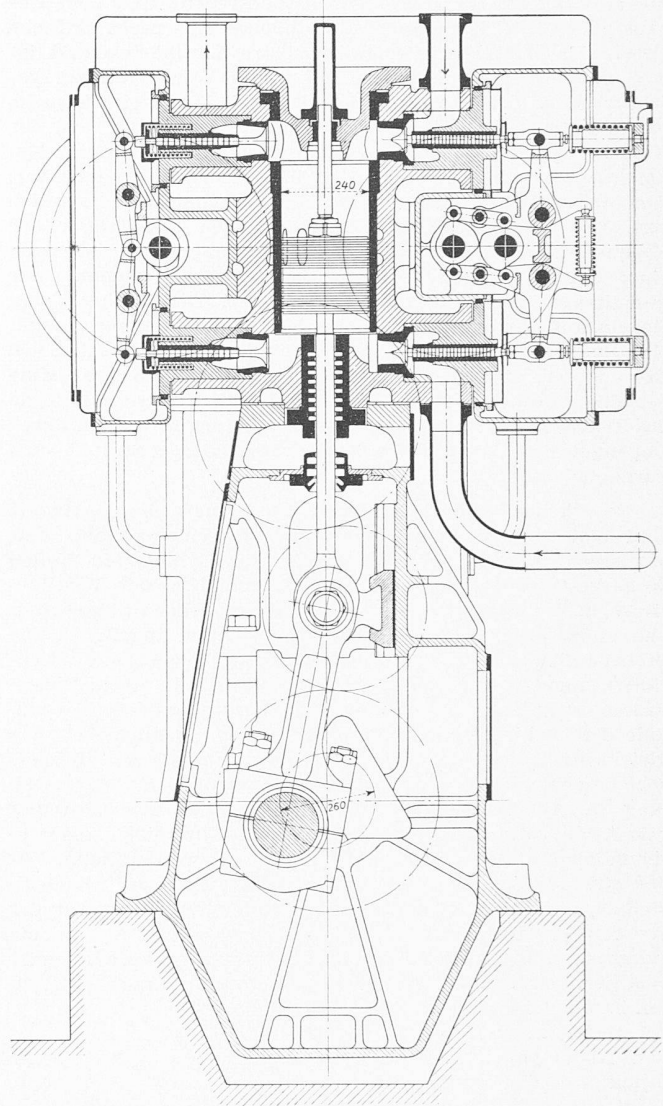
Dreizylinder-Hochdruckdampfmaschine, Querschnitt, Masstab 1:20
